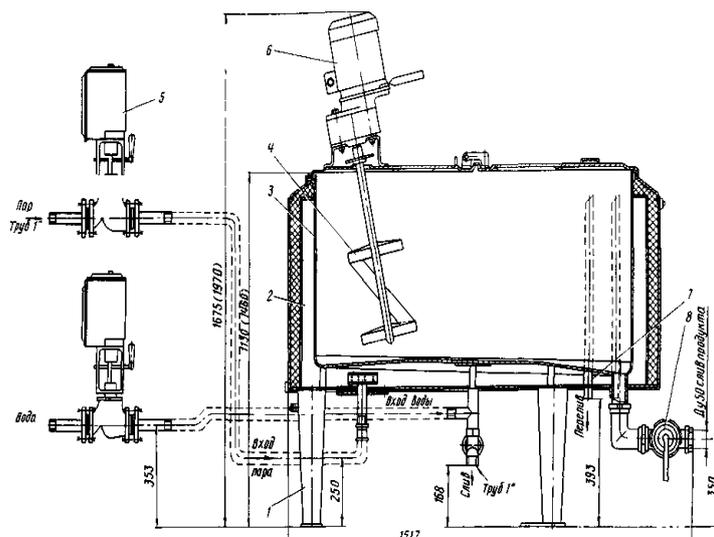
Общий вид ванны пастеризационной марки Г6-ОПА-600 (Г6-ОПБ-1000): 1 - опора; 2 - корпус; 3 - ванна; 4 - мешалка; 5 - электромагнитный вентиль; 6 - привод; 7 - переливная труба; 8 – кран
